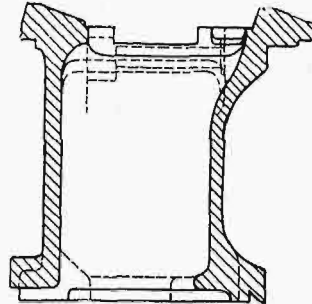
Łoże półautomatu wielonarzędziowego fabr. Le Blond Machine Tool Co. Cincinnati.
